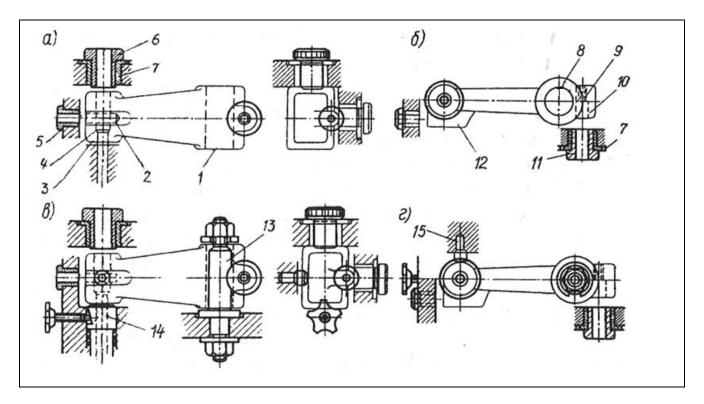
Последовательность проектирования приспособления-кондуктора для сверления трех отверстий
